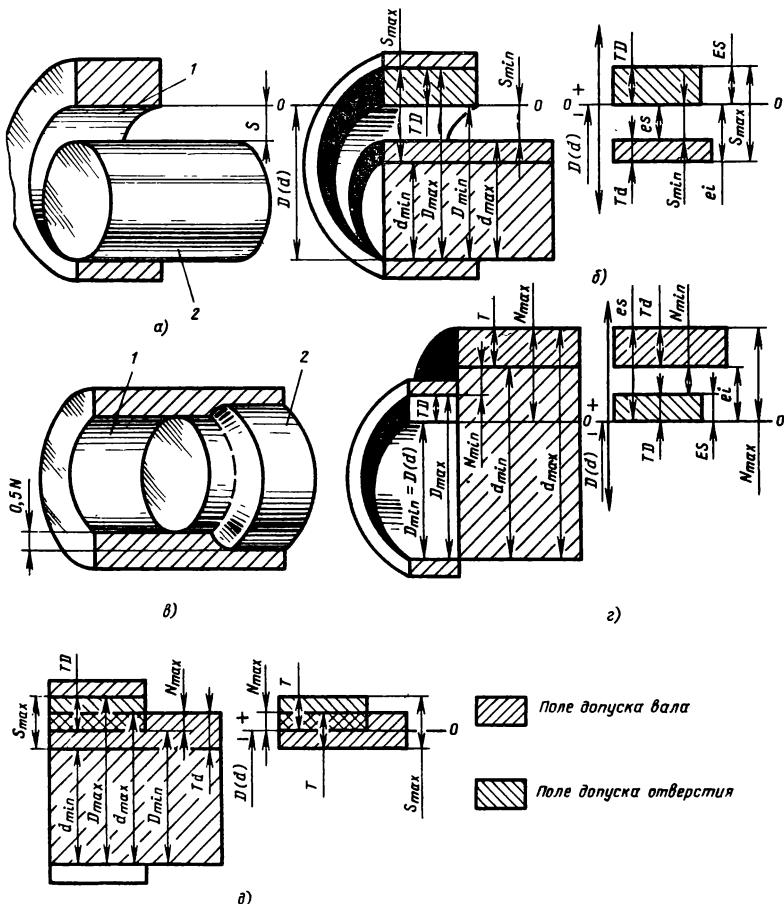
Соединение вала 2 и отверстия 1 с зазором S (*а*) и с натягом N (*б*); поля допусков посадки с зазором (*в*), с натягом (*г*) и переходной посадки (*д*)
